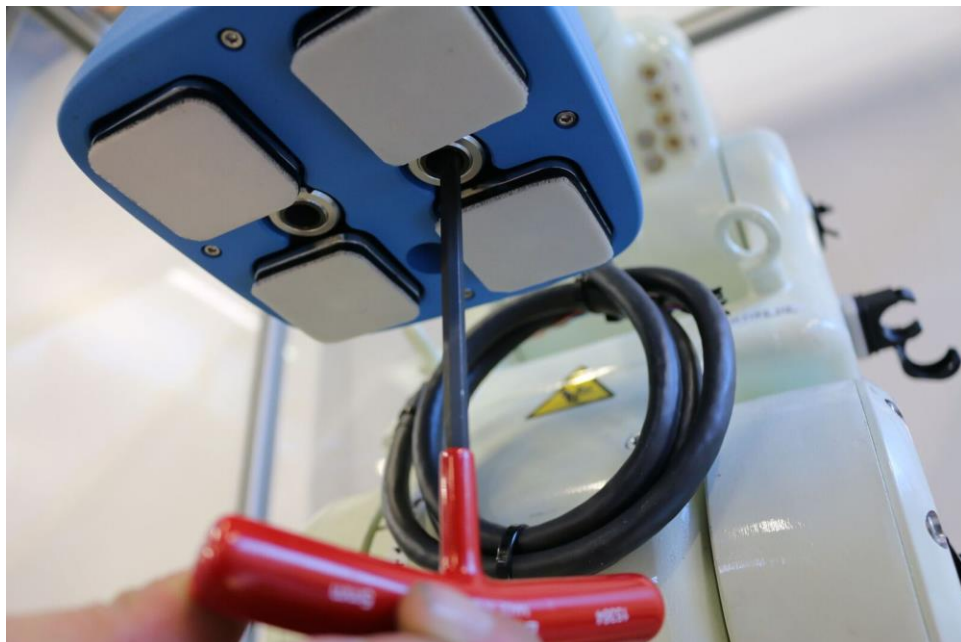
Monteringsplatta för alla märken förutom Universal Robots.
